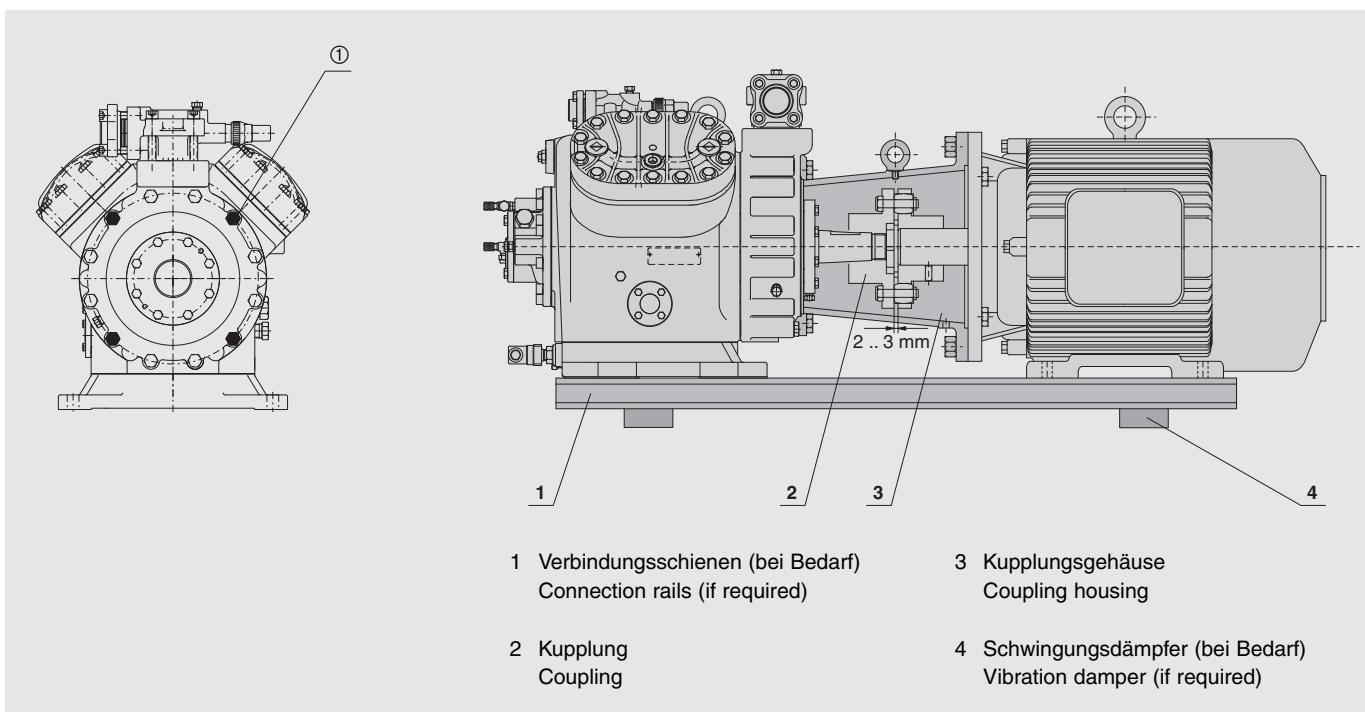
Motor-Verdichtersatz mit Kupplungsgehäuse
